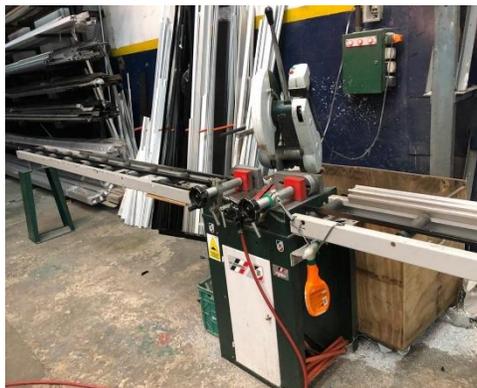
Máquina de corte cabezal simple para perfiles (Fuente: Propia)
